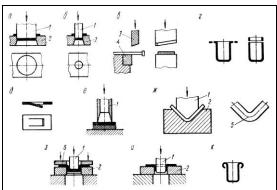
Операции листовой штамповки: а) вырубка; б) пробивка; в) отрезка; г) образка; д) надрезка; е) просечка; ж) гибка; з) вытяжка; и) отбортовка; к) закатка
